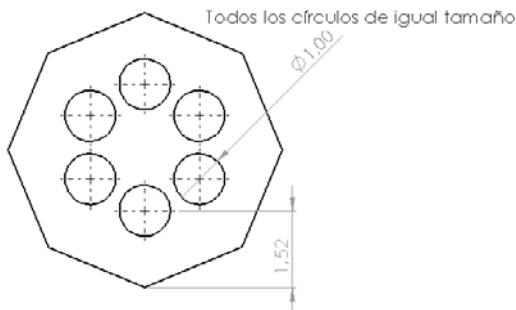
figura construida en IPS y con un valor de extrusión de 0,5 Pulgadas y la pieza se realiza en plano alzado.
